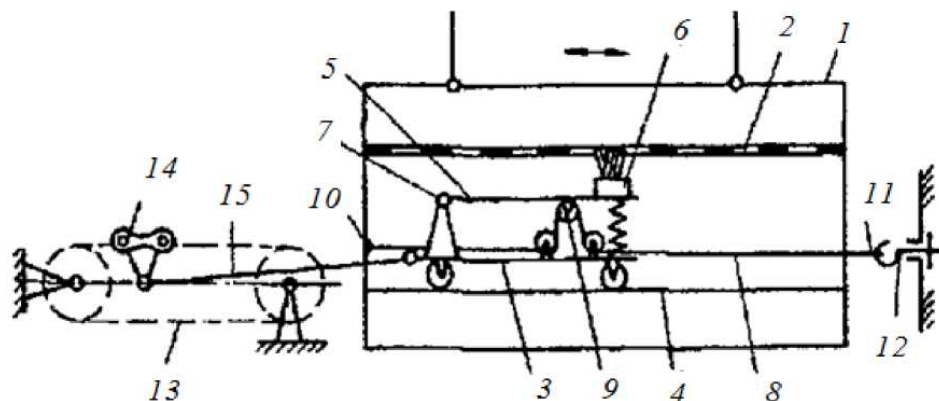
Механізм очищення решіт зерноочисних машин з коливальним рухом решітний стан: 1 - решітний стан; 2 - решето; 3 - платформа; 4 - напрямні; 5 - підпружинений важіль; 6 - щітка; 7 - шарнір; 8 - трос; 9 - блочки; 10,11 - кінці троса; 12 - механізм натяження; 13 - ланцюгова передача; 14 - ланка ланцюгової передачі; 15 – тяга
